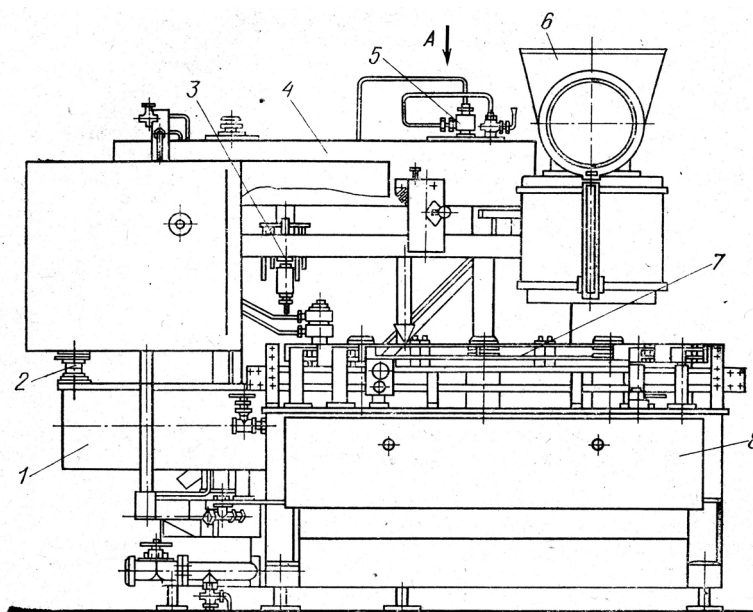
Розливочно-закупорювальний блок марки РЗ-ВМБ-40/6:
